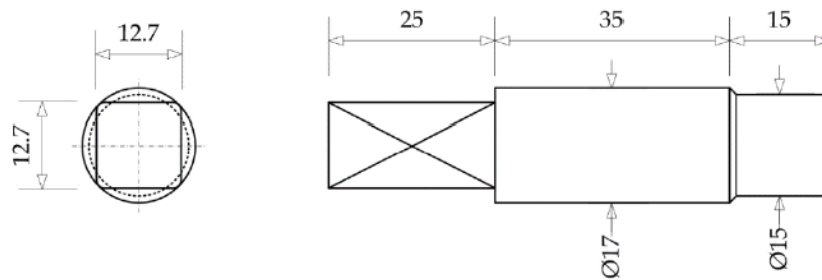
Geometria e dimensões de um provete (meio substrato com dimensões em mm) [6]
